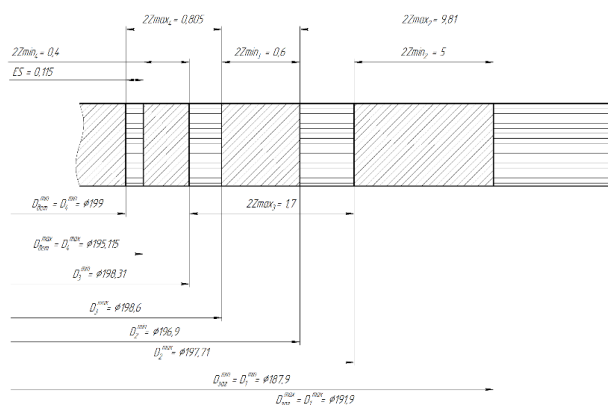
Схема припусків для обробки поверхні 1 – внутрішньої циліндричної $\text{Ø}199^{+0,115}$
